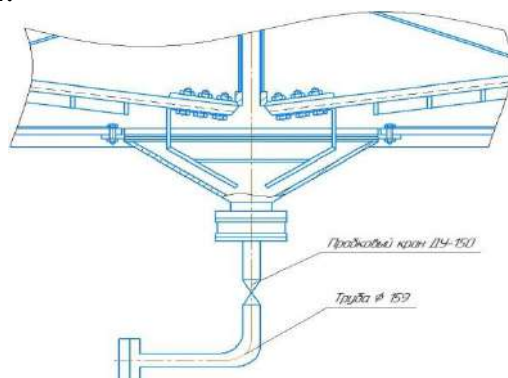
Реконструкция разгрузочной части конуса сгустителя
